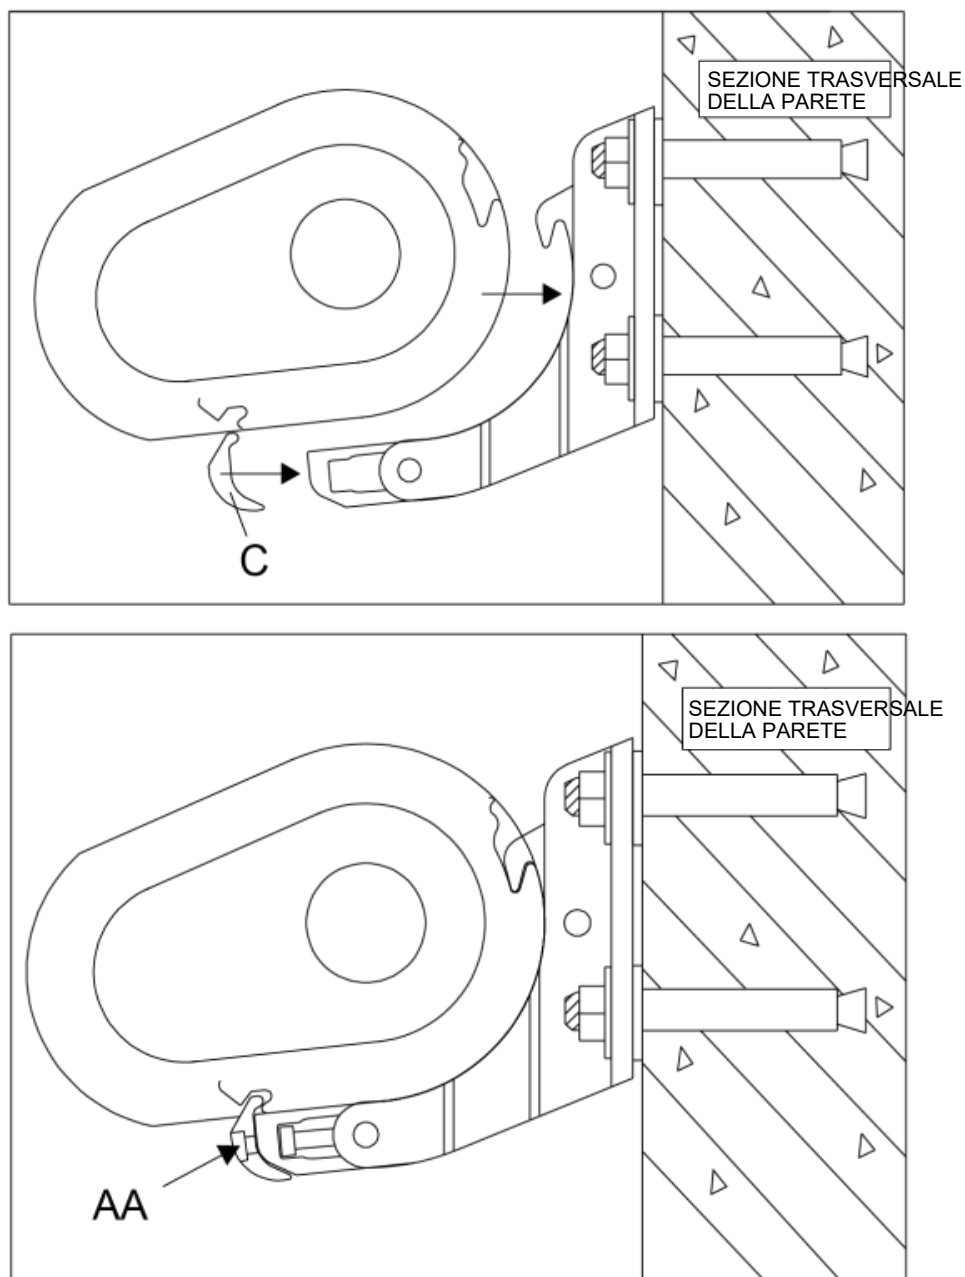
Fissare la parte di collegamento (C) alla cassetta e alle staffe tramite il bullone (AA).
